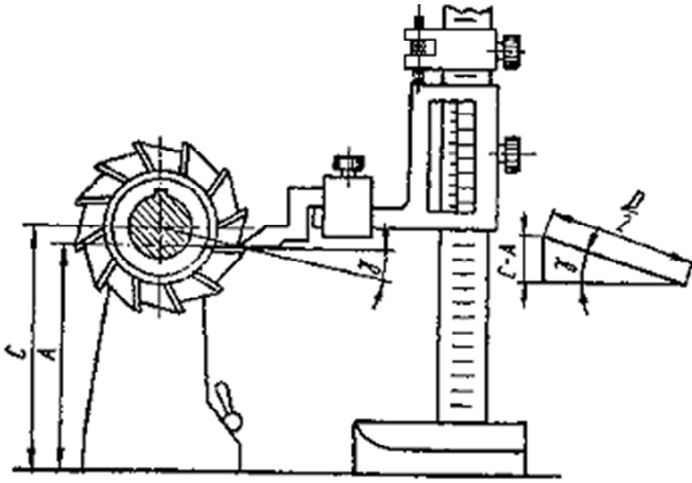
Контроль переднего угла фрезы штангенрейсмасом
